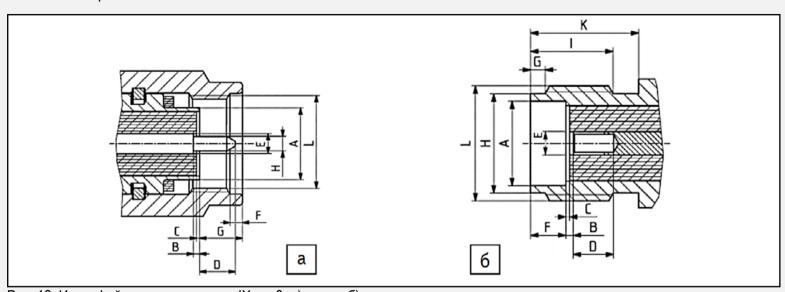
Интерфейс соединителя тип ІХвар.3: а) вилка; б) розетка
